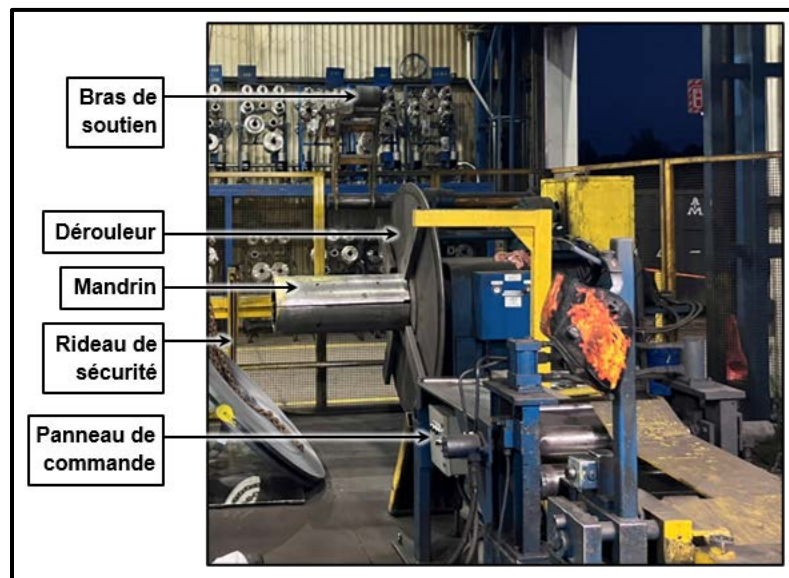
Composantes du dérouleur de bobines d'acier
